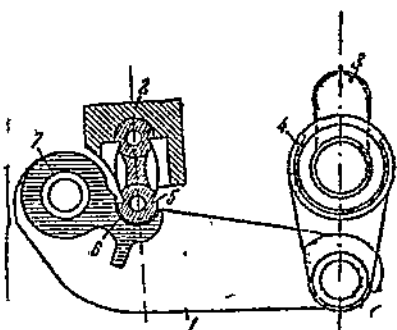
Схема соединения прессующего поршня с прессующим рычагом:
